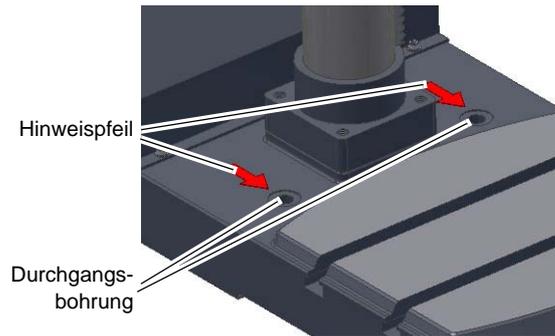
Kennzeichnung der Befestigungspunkte an Tischbohrmaschinen
